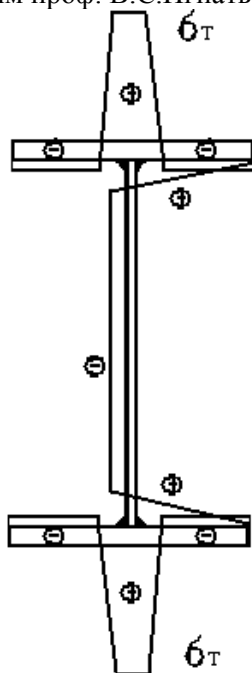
Вид эпюры остаточных напряжений в сварном двутавре
